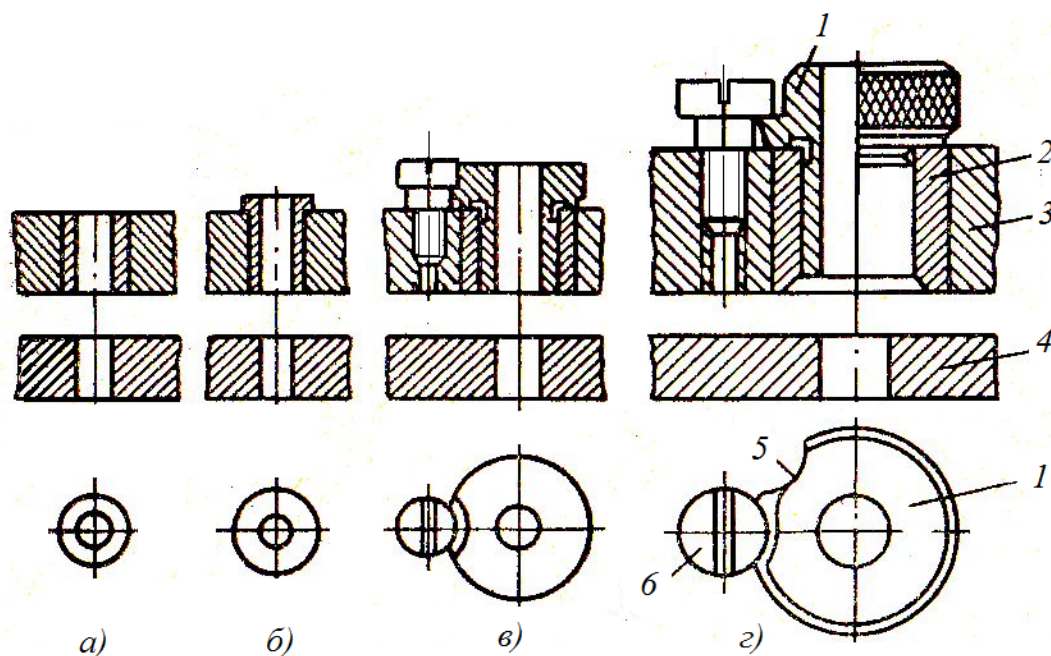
Общий вид стандартных кондукторных втулок:
